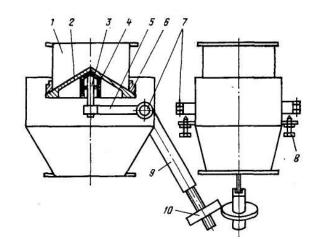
Мигалка с горизонтальным затвором: 1 – приемный патрубок; 2 – клапан конусный; 3 – игла опорная; 4 – стакан; 5 – рычаг; 6 – седло; 7 – ось; 8 – винты регулировочные; 9 – рычаг; 10 – груз
